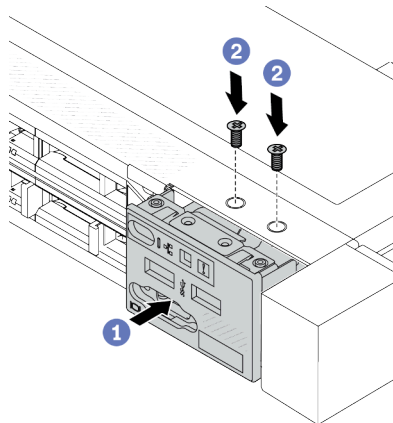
Instalar um módulo de E/S frontal no chassi de 2,5 pol.
